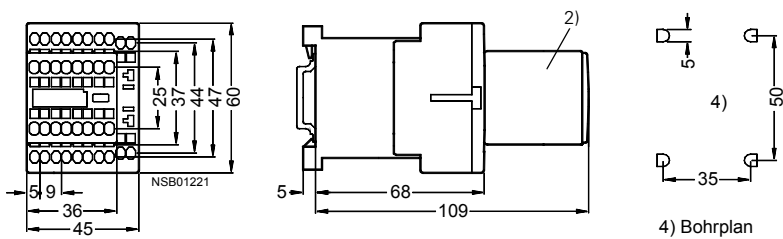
Schütze 3RT10 1 (Cage Clamp-Anschluss) mit Hilfsschalterblock
